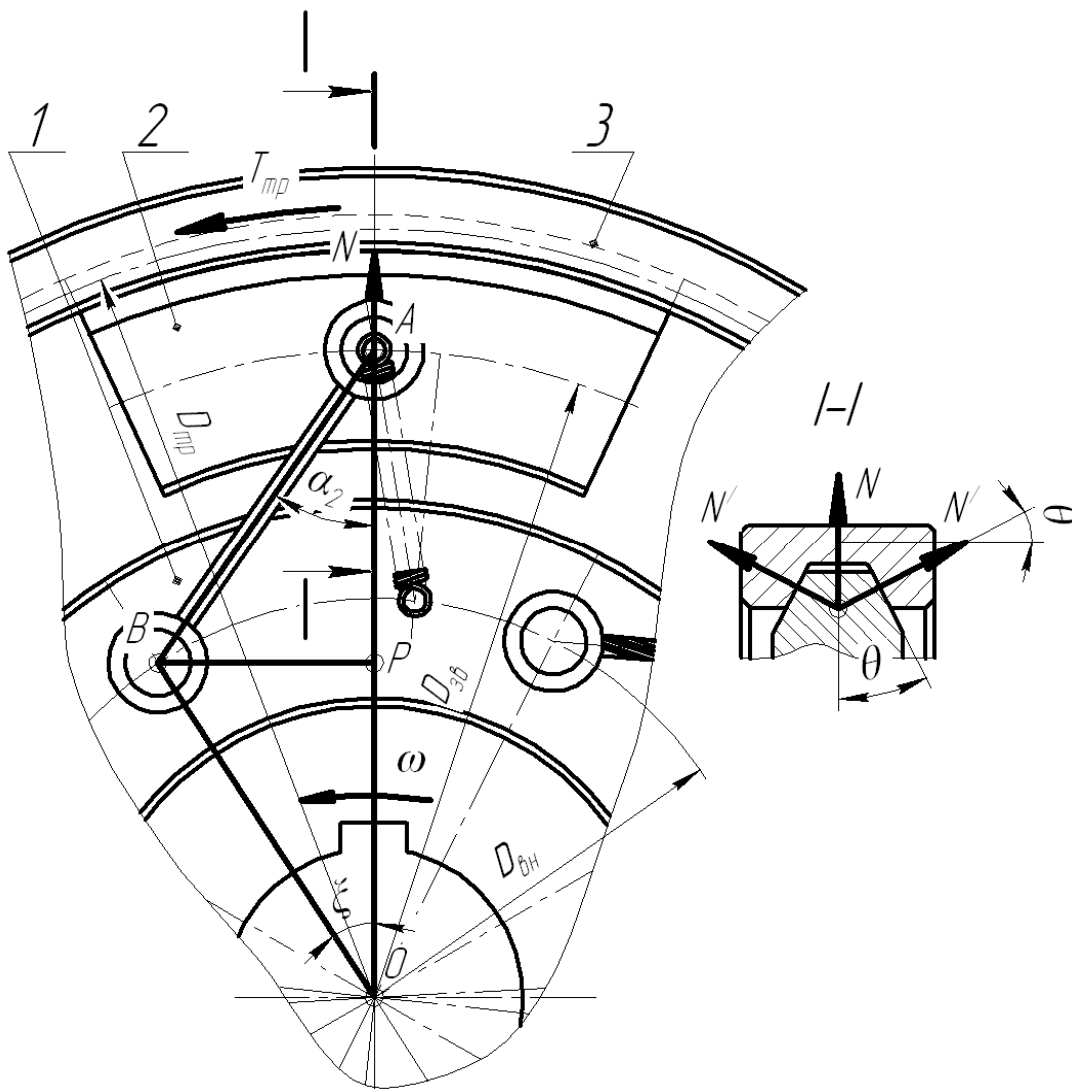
Розрахункова схема фрикційної колодкової муфти з конусними поверхнями тертя та канатними елементами
